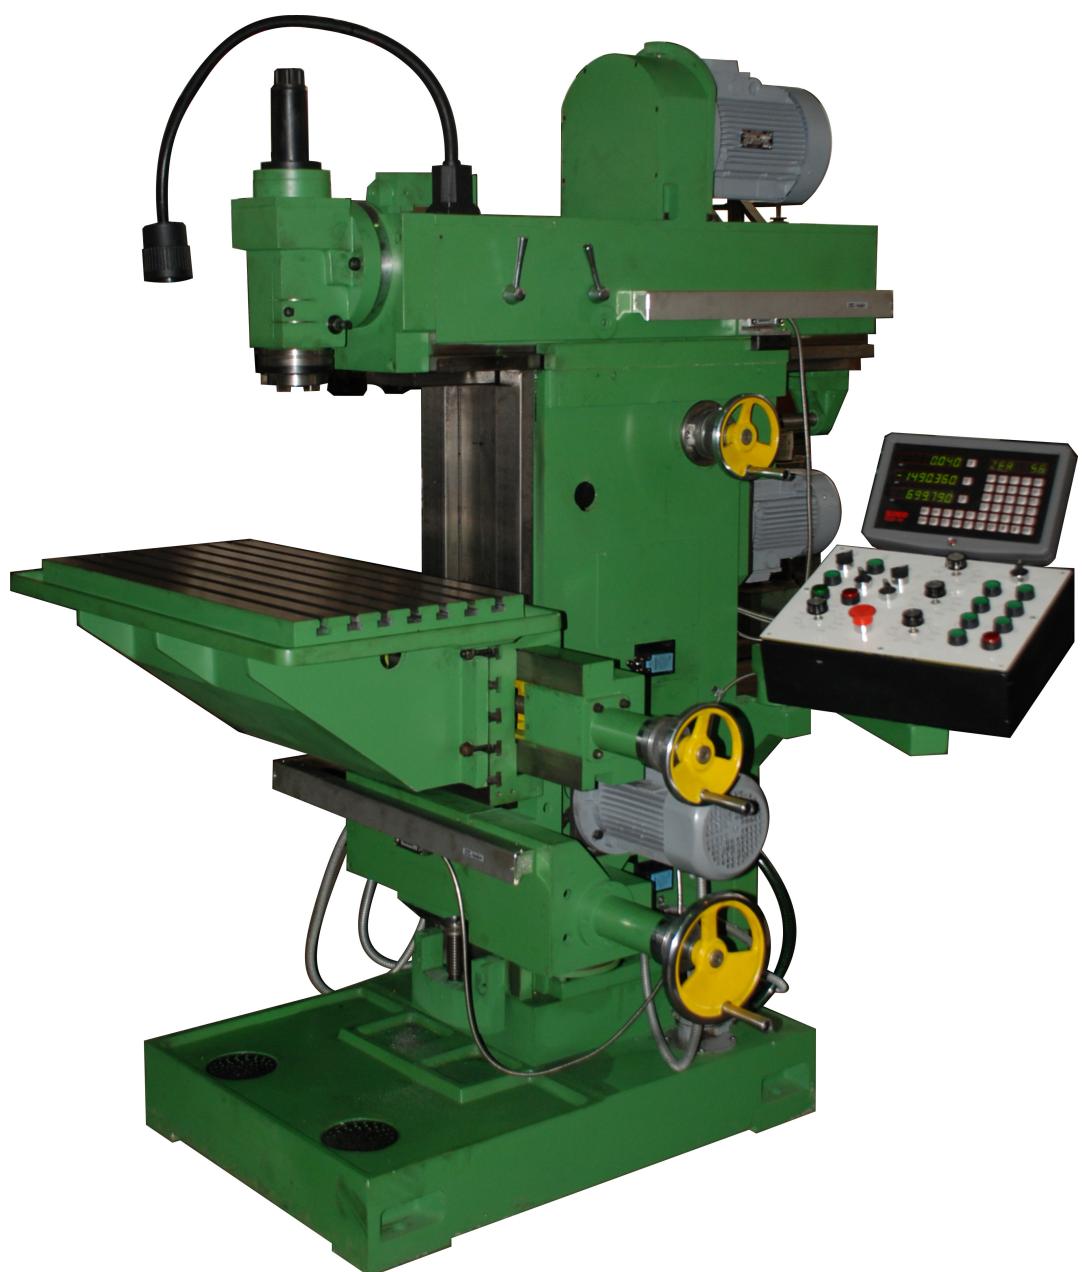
Станок фрезерный широкоуниверсальный инструментальный
